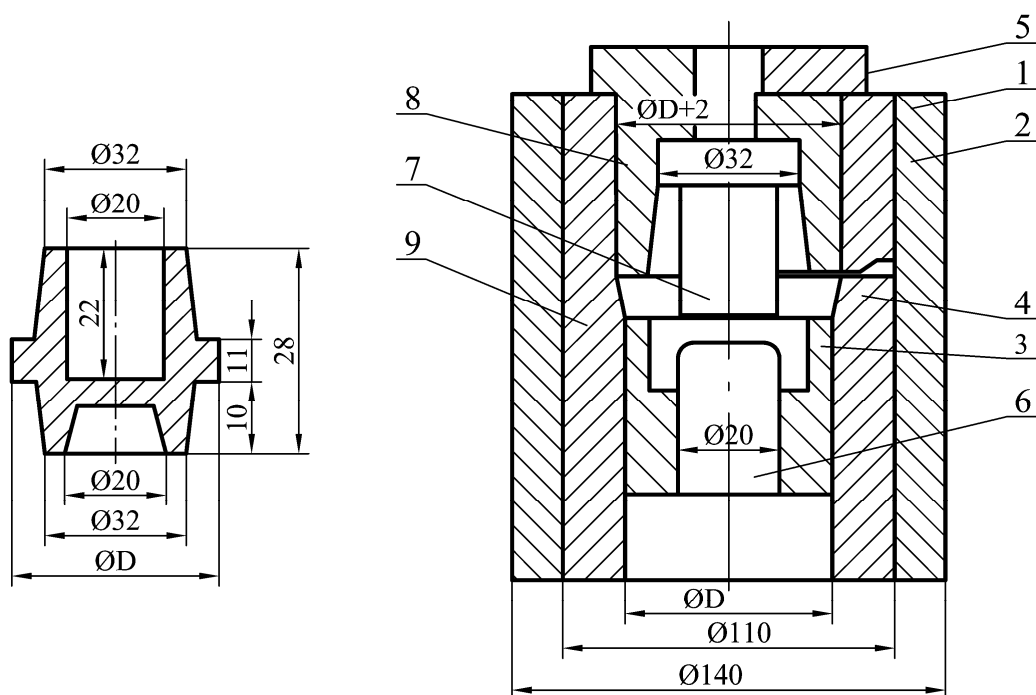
Чертежи поковки и приспособления для открытой и закрытой штамповки
